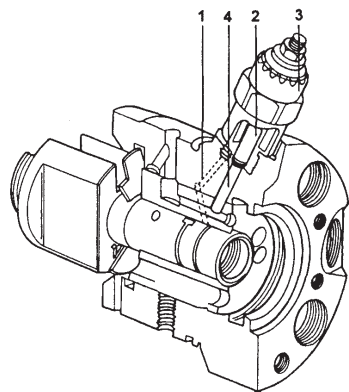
Детали привода ТНВД Lucas DPC с плавающей муфтой:
